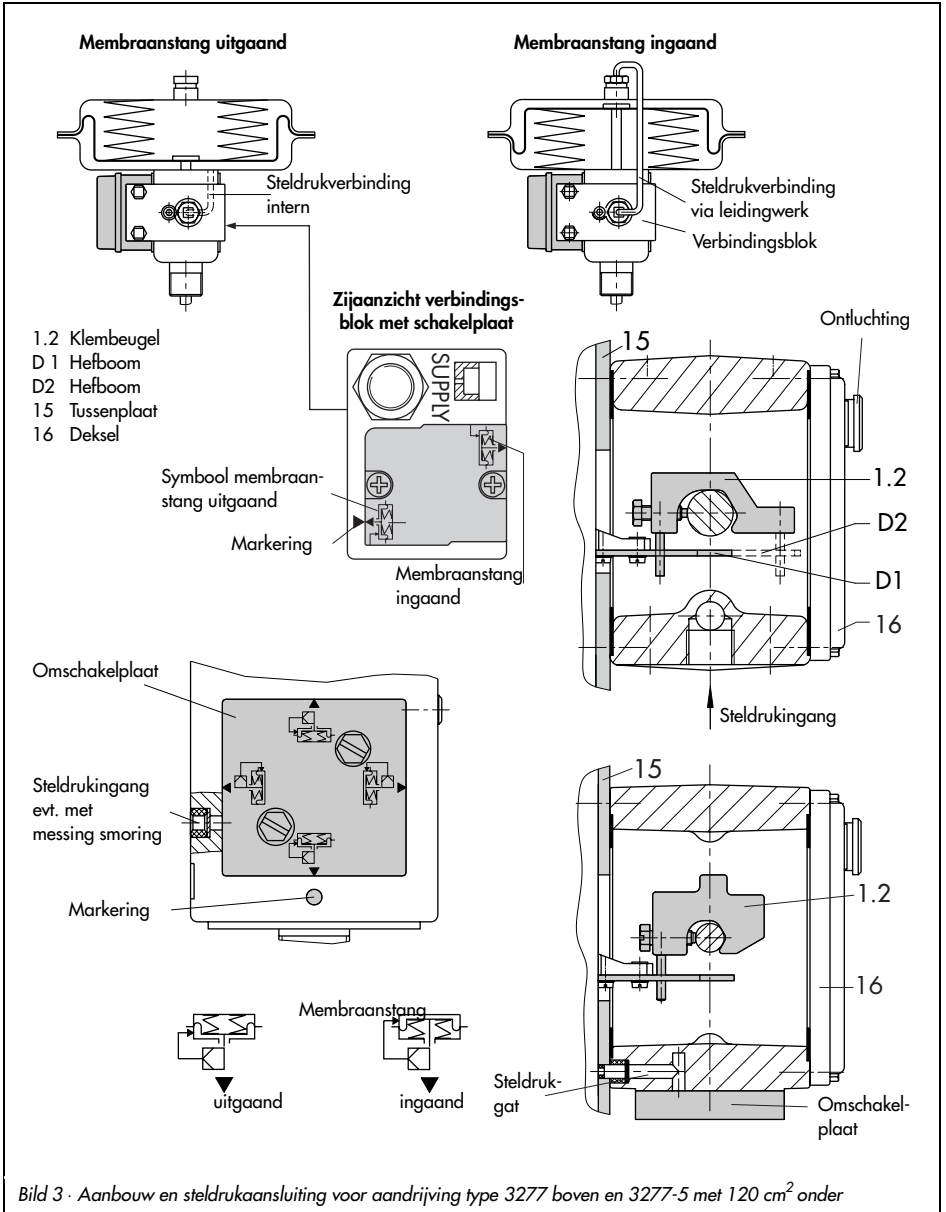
· Aanbouw en steldrukaansluiting voor aandrijving type 3277 boven en 3277-5 met 120 cm² onder
